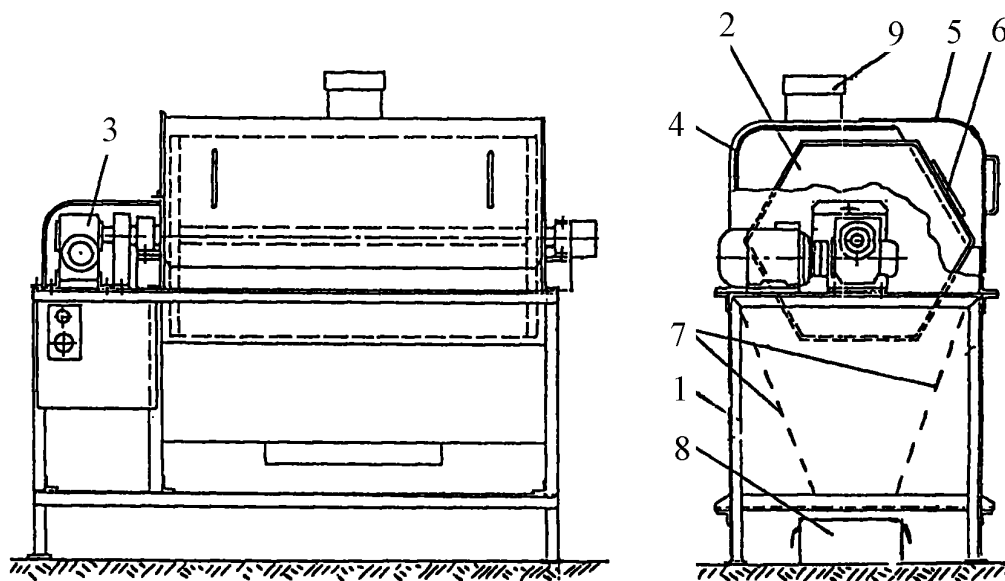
Барабан для отбивки шишек БОШ-4: 1 – рама; 2 – отбивочный барабан; 3 – электропривод; 4 – кожух; 5 – съемная крышка; 6 – люк-затворка; 7 – лотки; 8 – ящики; 9 – патрубок
